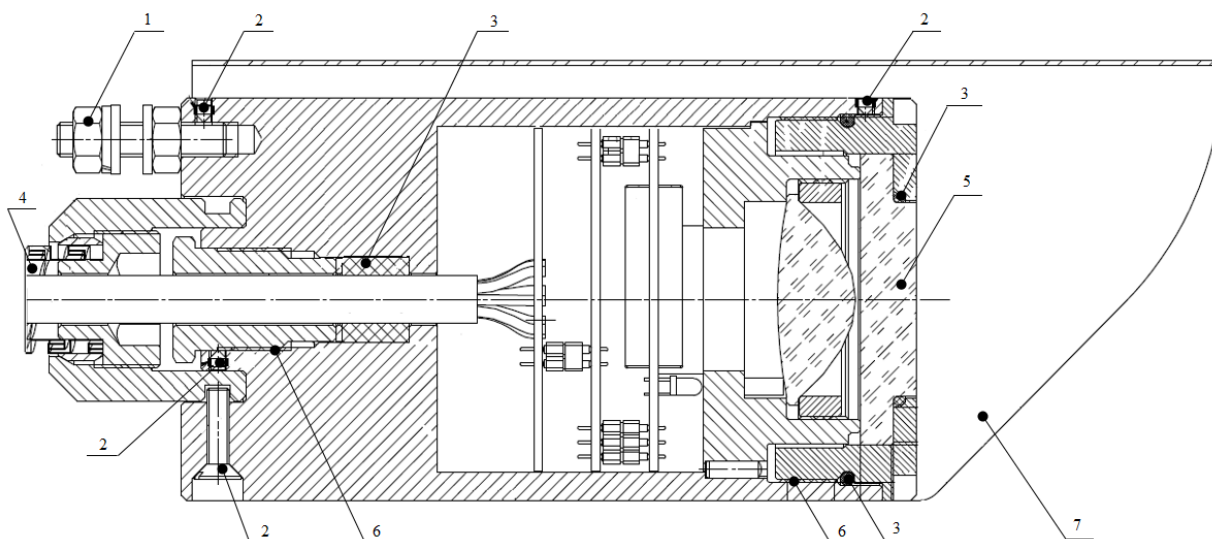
Схема конструкции корпуса блока извещателя охранного активного линейного оптико-электронного:
